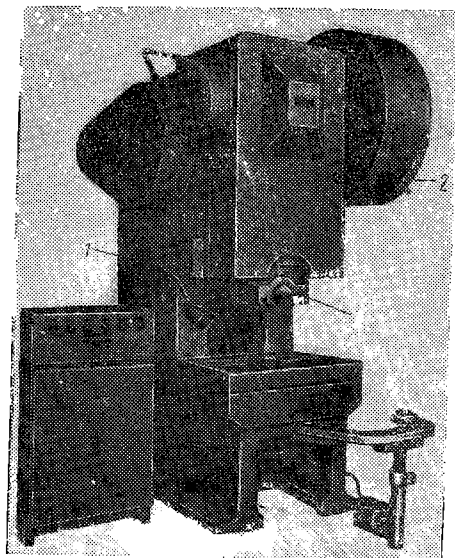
Двухстоечный однокривошипный пресс простого действия К2130 усилением 100 тс: 1 — станина, 2 — маховик (закрывает кожухом), 3 — ползун
